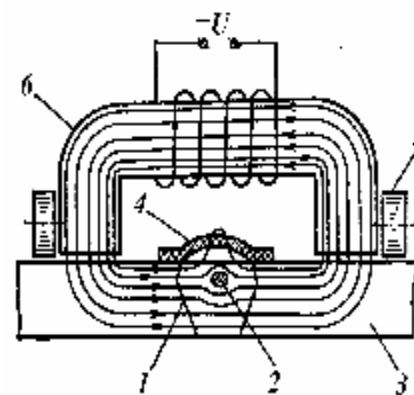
Схема намагничивания сварного шва вместе с магнитной лентой: 1 – сварной шов; 2 – дефект; 3 – деталь; 4 – магнитная лента; 5 – ролики; 6 – электромагнит
